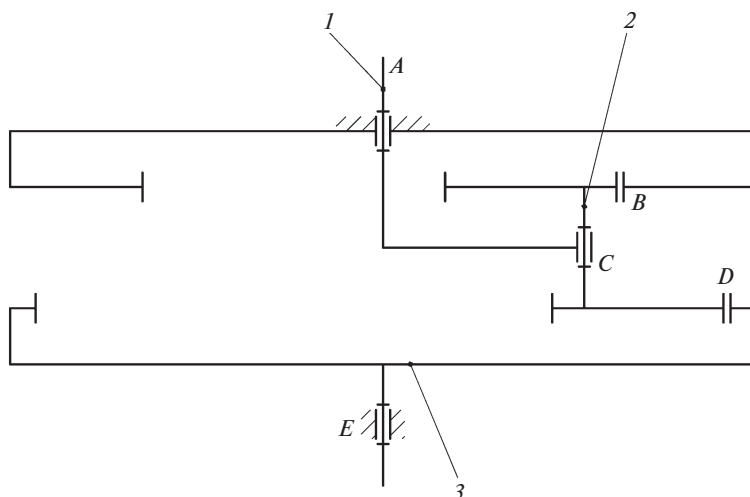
Структурная схема планетарного механизма с некруглыми зубчатыми колесами.
